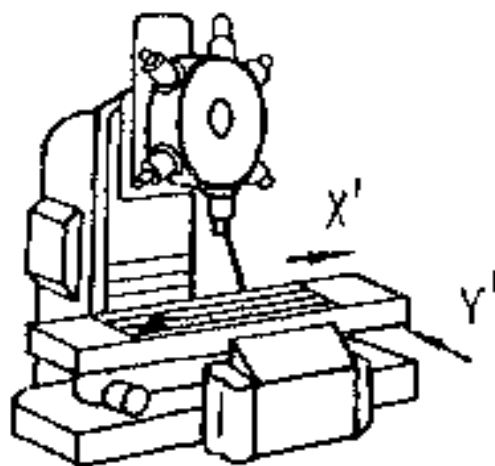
Компоновка безконсольного вертикально-фрезерного верстата з револьверною головкою.
